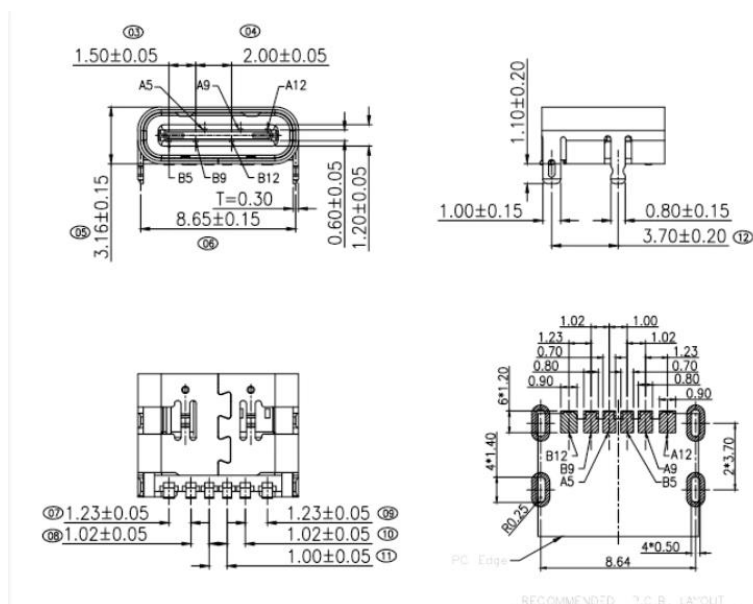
Габаритні розміри роз'єма USB Type-C фірми LeT
